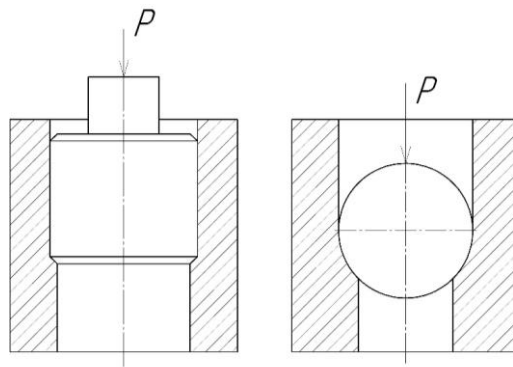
Калибрование с использованием ролика и шарика
